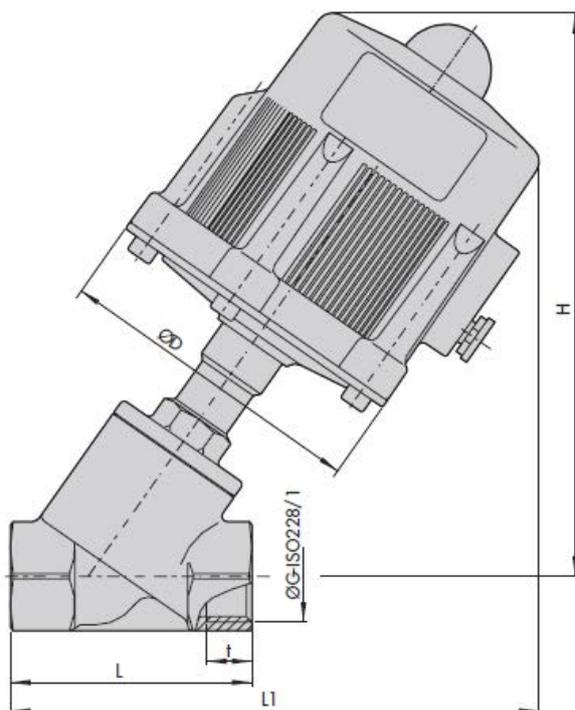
Проходной клапан Тип 3353 с внутренней резьбой
